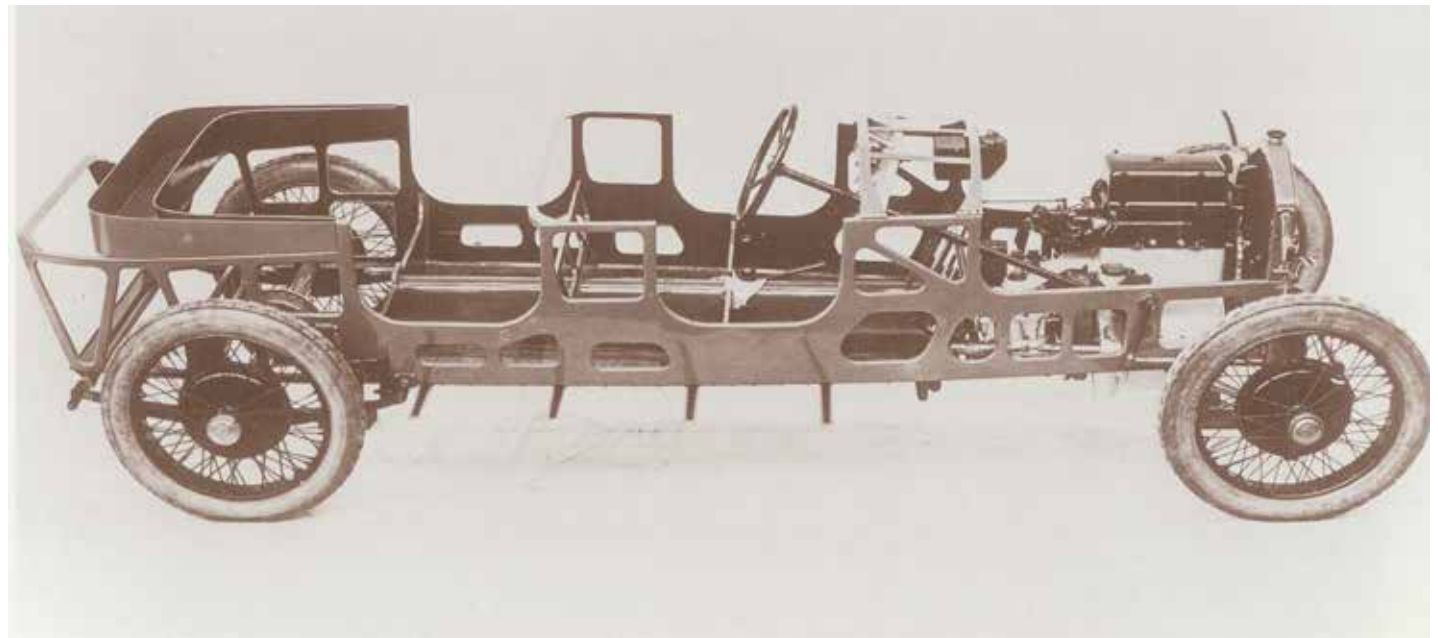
Struttura della Lambda con tutta la meccanica a Parigi all'inizio di ottobre 1922
